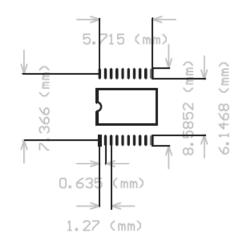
USB2I2C SSOP20 PCB 封装图 (MM)
